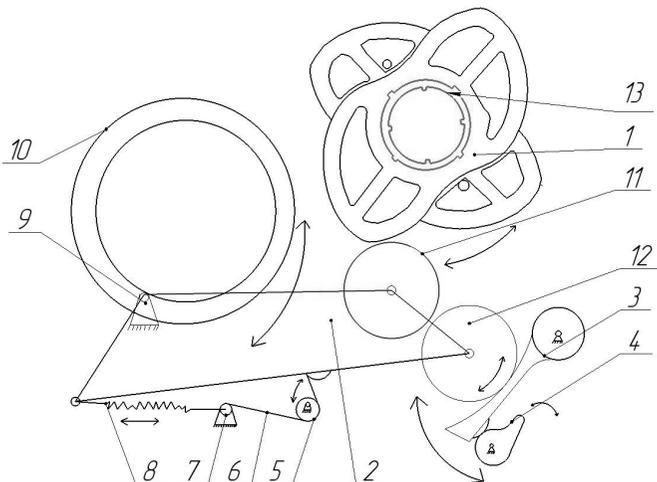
Общая кинематическая схема редуктора высевающего аппарата сеялки:
